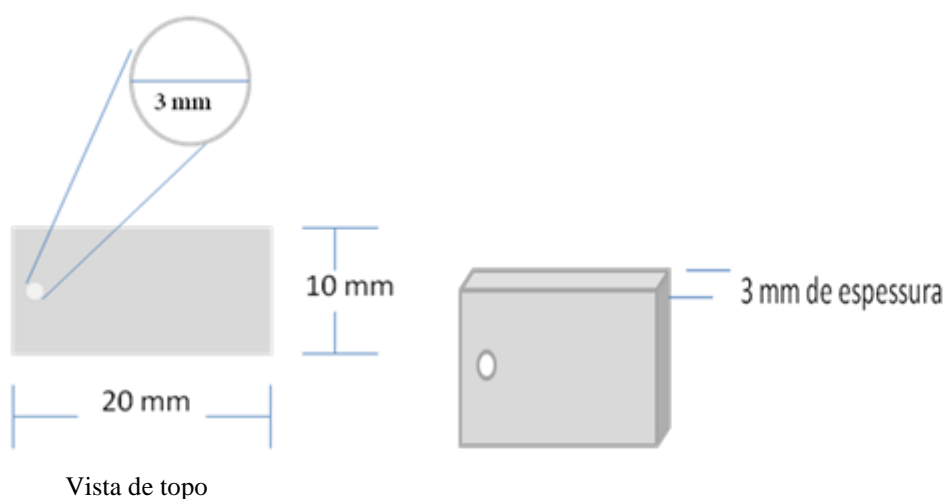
Vista de topo e lateral do corpo de prova (dimensões em milímetros).
